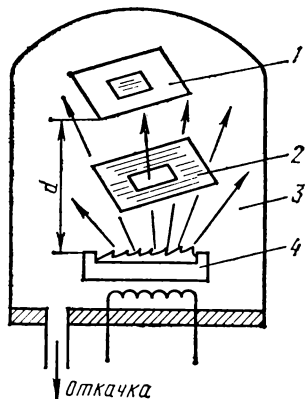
Схема рабочей камеры установки вакуумного напыления:
